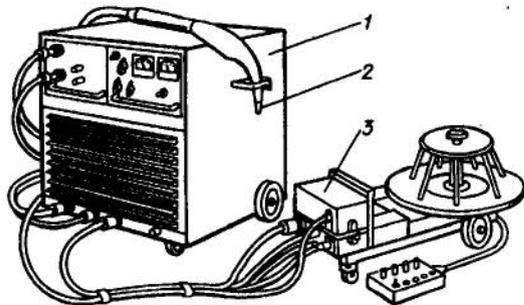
Зварювальний напівавтомат ПДГ-601:
